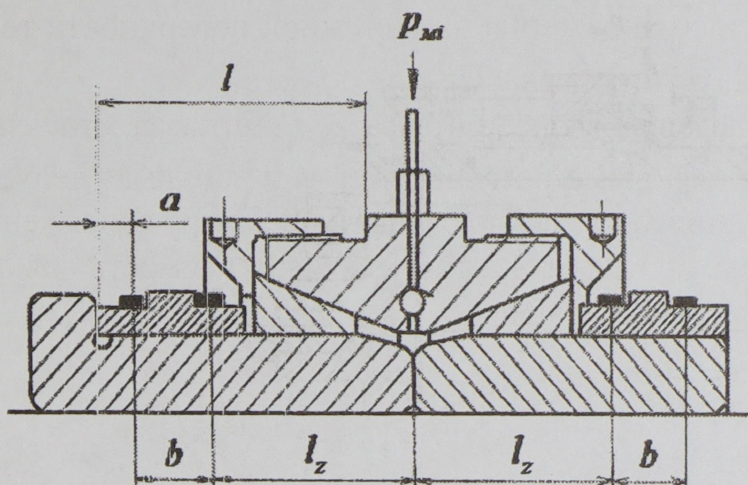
Схема осуществления неразрушающего контроля прочности напрессовки колец подшипников (Патенты на изобретения ВУ 13116 С1, RU 2329478 С1)
